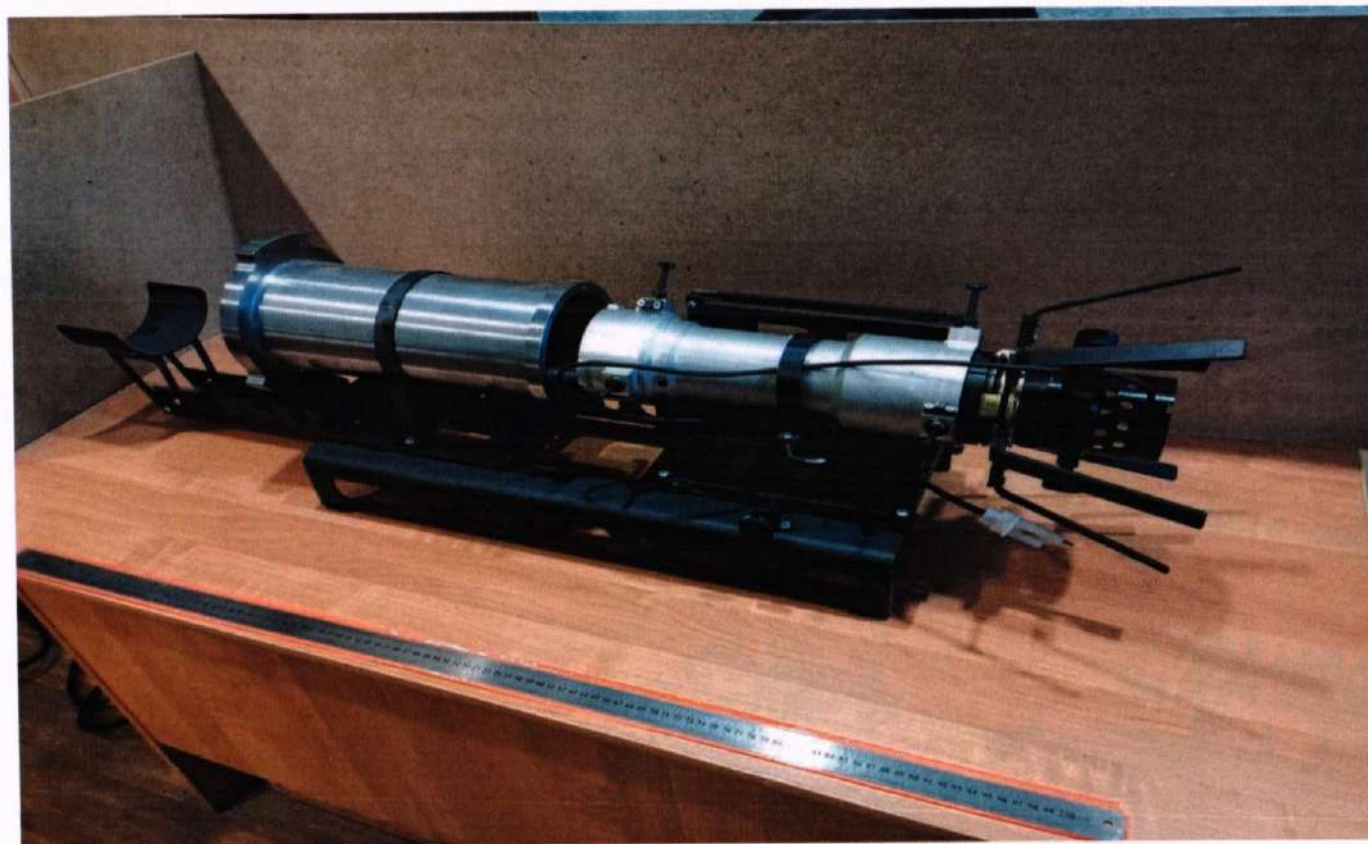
Приспособление поверочное ПИКА-АС1М6.06.000
